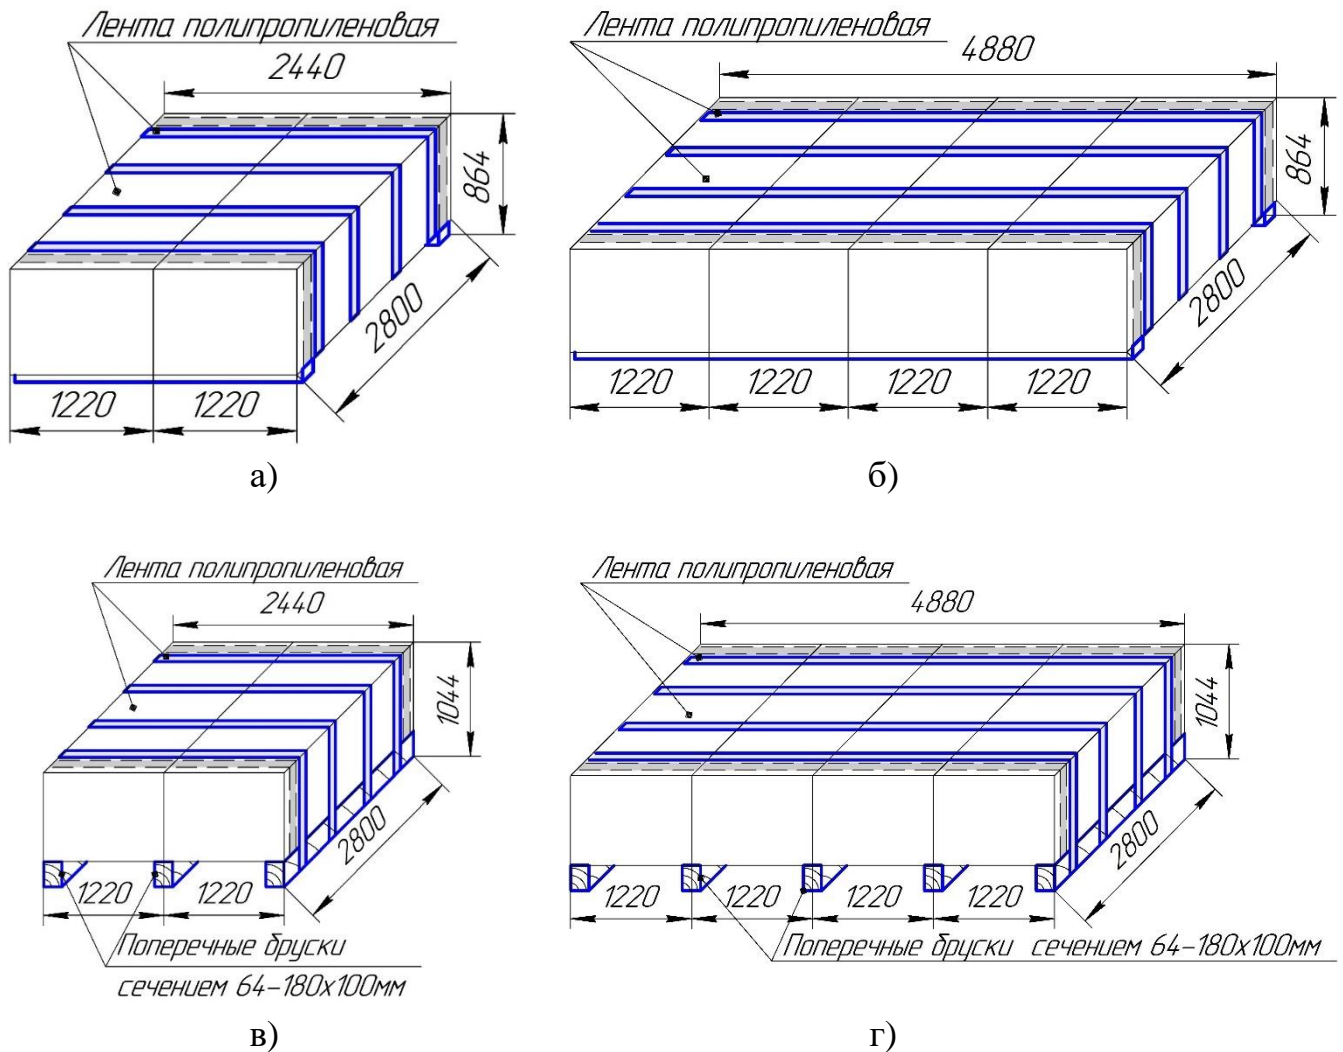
Вид транспортного пакета плит размером 2440-4880x2800мм
